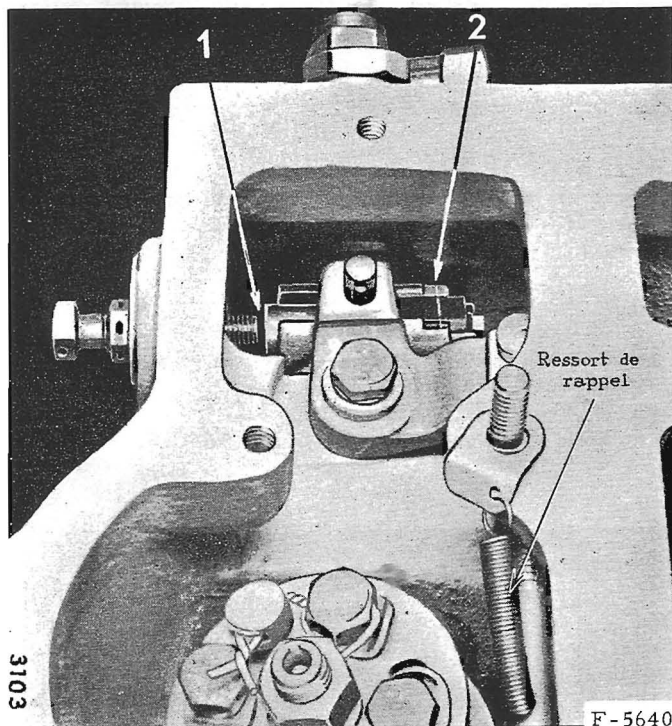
(1) Jeu entre crémaillère et vis butée
